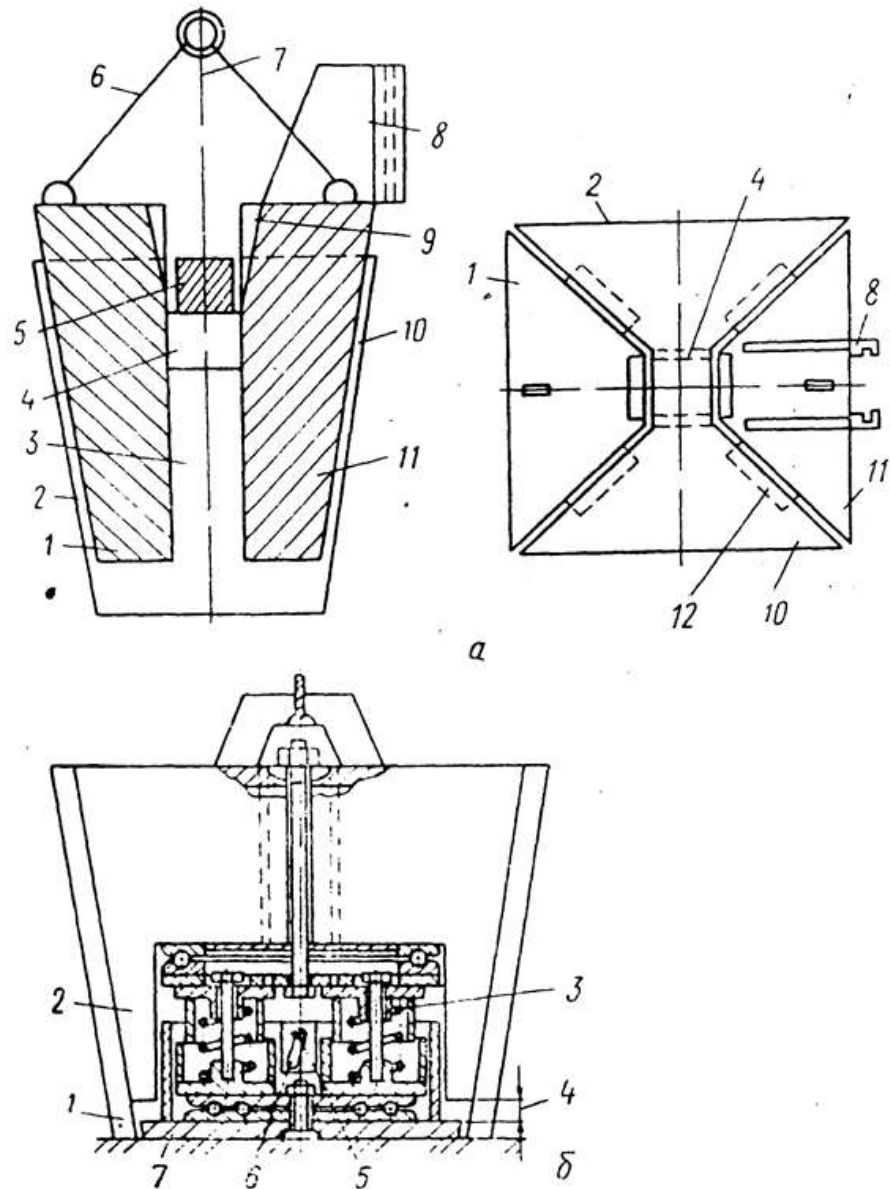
Пристрої для виштамповування поглиблень[6]:
